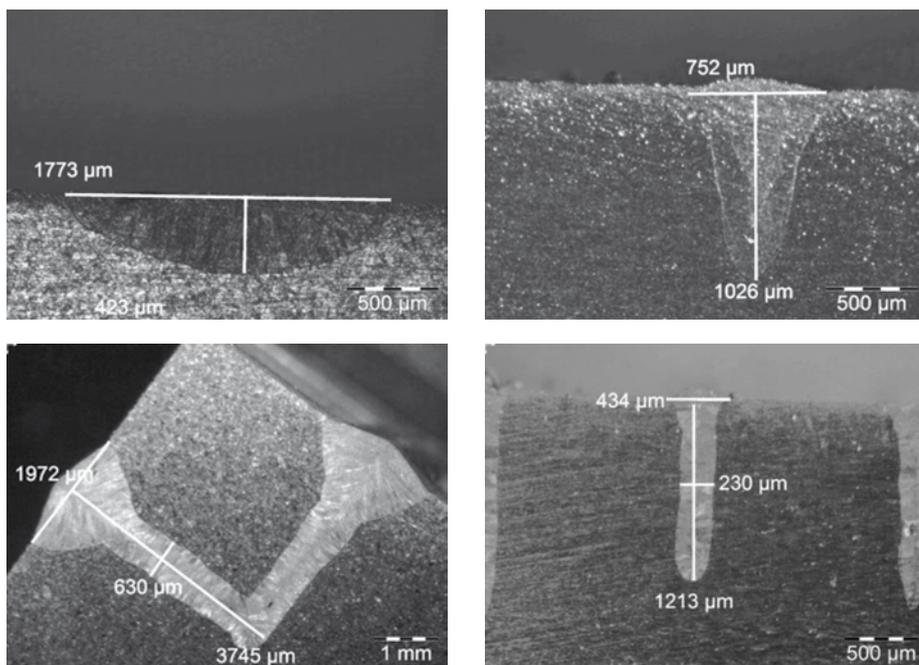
Verbunde aus einer Laserschweißung: sehr flache und breite Naht (oben links); dreieckiger Nahtquerschnitt (oben rechts); tiefe und schmale Naht mit Aufweitung an der Oberfläche durch beginnende Wärmeleitung aufgrund geringer Schweißgeschwindigkeit (unten links); sehr schmale Naht mit rechteckigem Querschnitt (unten rechts)
